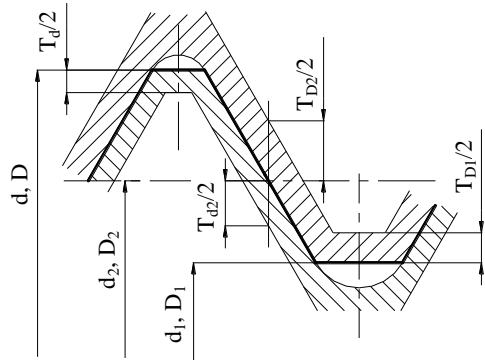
Схема полів допусків метричної різьби
